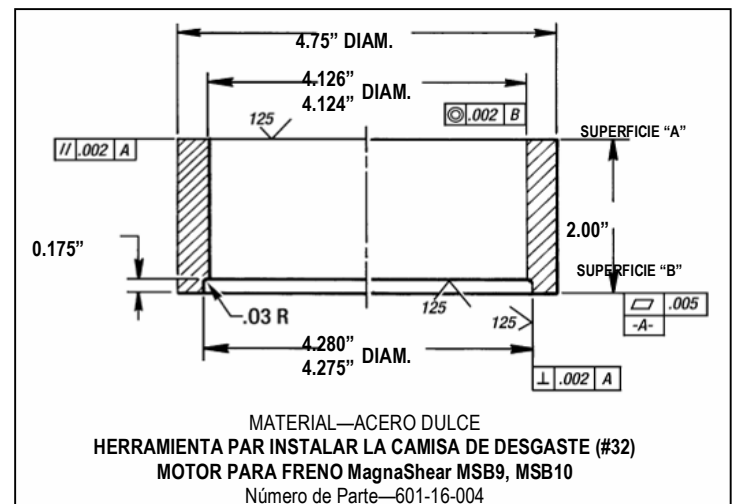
Herramienta para Instalar la Camisa de Desgaste
